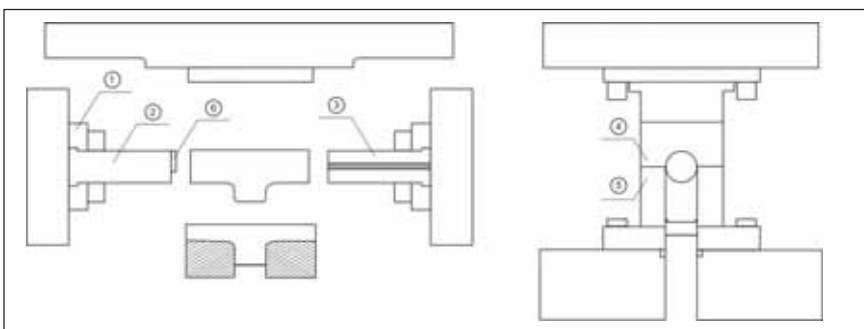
Общий вид штампа для гидроформовки тройника и готовая деталь
